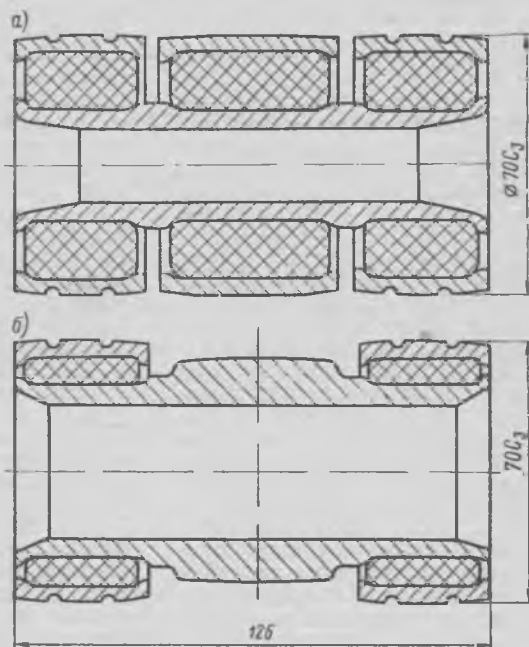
Упругие элементы зубчатого колеса: мягкий (а) и упорный (б)
